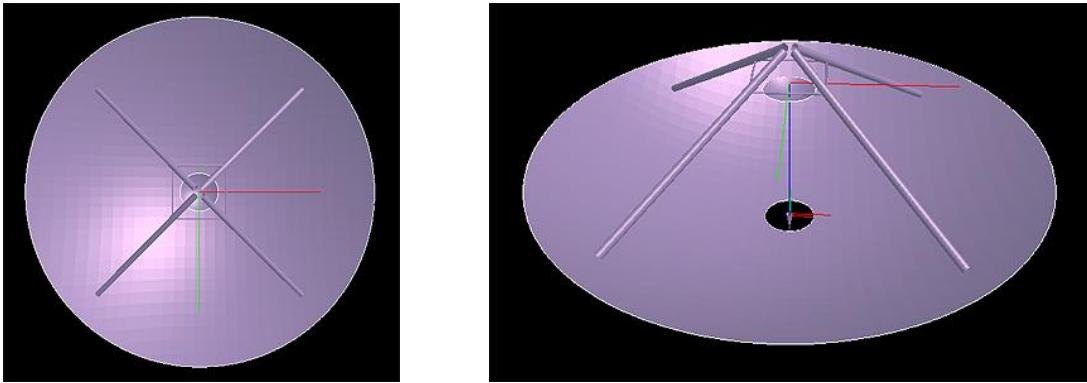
Disposizione degli struts. La disposizione è simmetrica rispetto all'asse focale.
